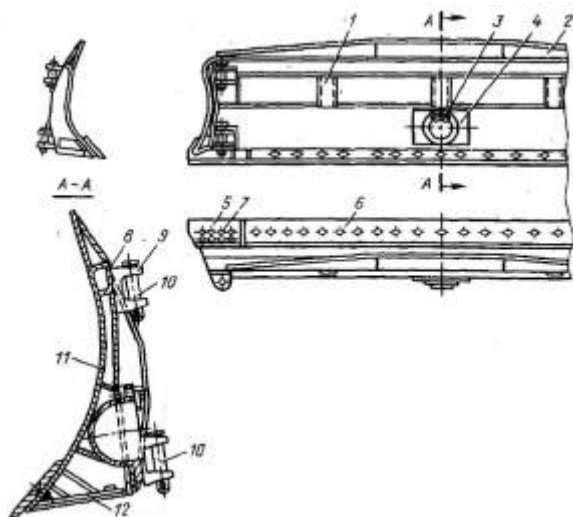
Отвал бульдозера ДЗ-17: 1 — вертикальная связь; 2 — козырек; 3 — крышка; 4 — гнездо; 5,7 — крайние ножи; 6 — средний нож; 8 — уголок верхней коробки жесткости; 9 — проушина; 10 — пальцы крепления раскоса и толкателя; 11 — лобовой лист; 12 — нижняя коробка жесткости.
